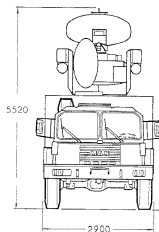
Abmessungen FlaRaKRad, Frontansicht
